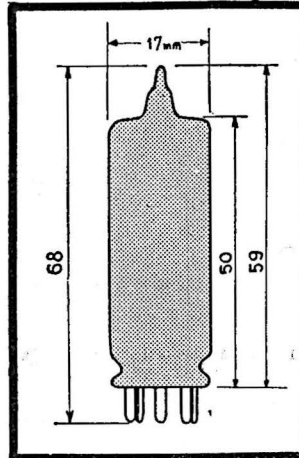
Fig. E. — Dimensions des tubes chauffés sous 35 et 50 V.
